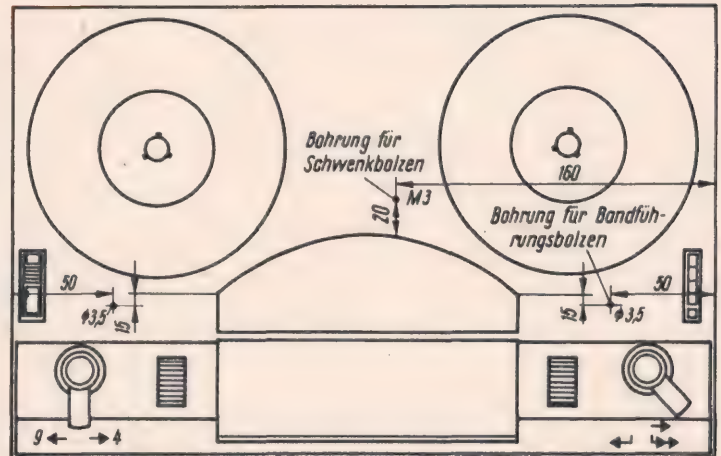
Lageskizze der Bohrungen für die Bandführungsbolzen auf dem Chassis des „B 5“
